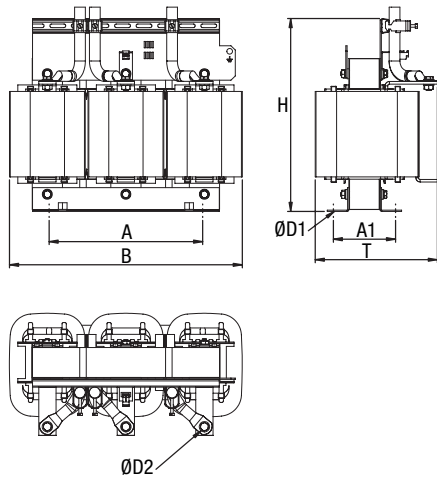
Maßzeichnung Hochsetzdrossel beispielhaft für BG7
